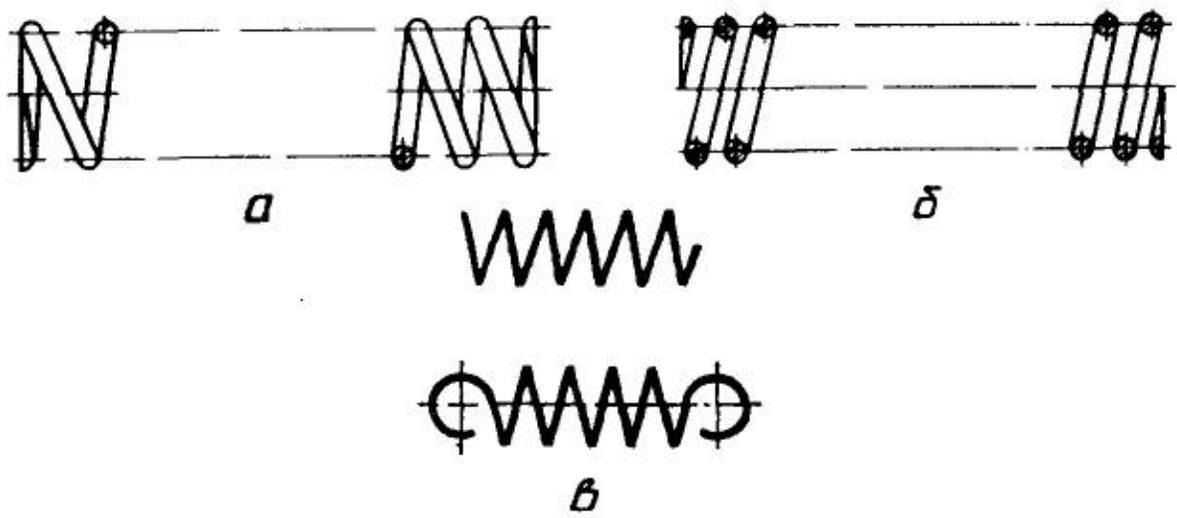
Умовне зображення пружин: *a* — виглядом; *б* — розрізом; *в* — схематичне.
